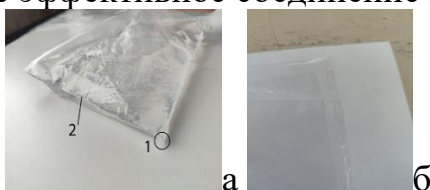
а) образец соединения пленочного материала на 1 – угловое соединение 90° , 2 – спаянный шов, выполненный с помощью отрезного ролика в 15° ; б) сплошной запаивающий шов
